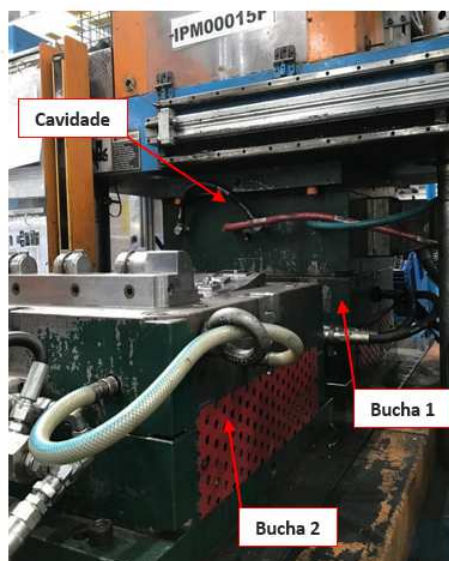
Máquina de Injeção de Plástico MultiPLAS V4-SD 160T e elementos do molde.
